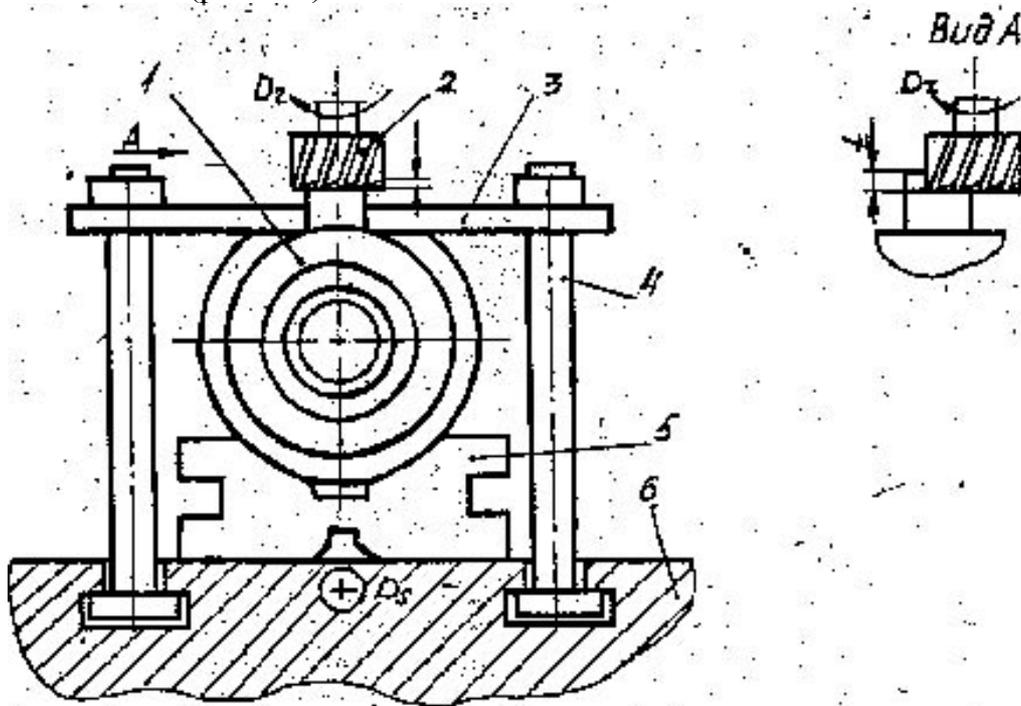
Схема фрезерования горизонтальной плоскости:
